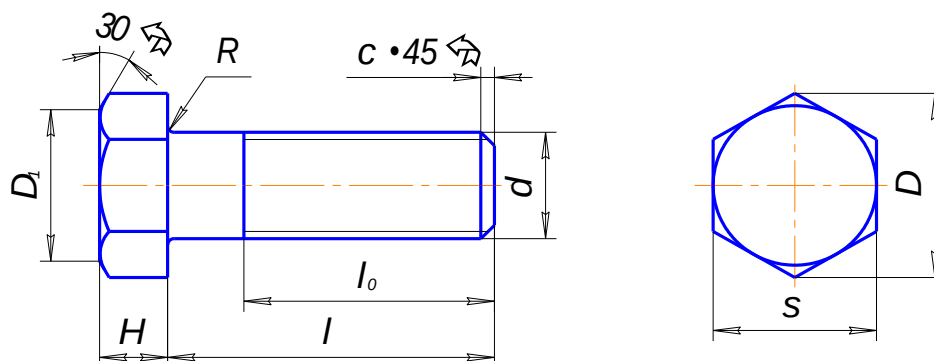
Образец выполнения сборочного чертежа резьбовых соединений
